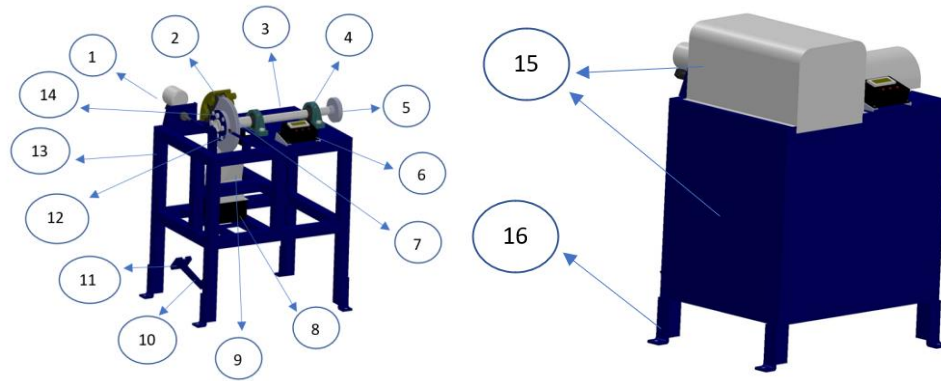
Sistema de freno hidráulico del banco de pruebas de motor de combustión interna de la Universidad Politécnica Salesiana.
